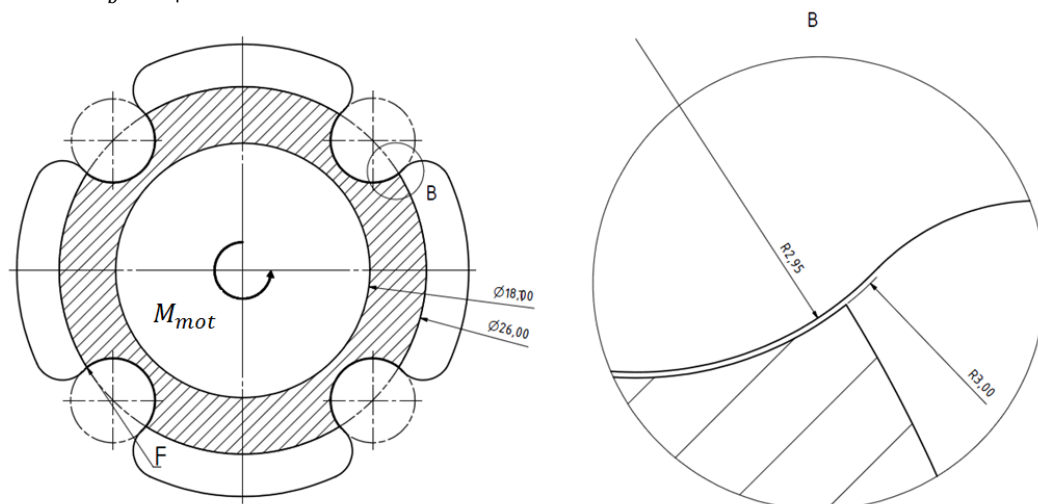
Führungsbolzen mit rinnenförmigen Nuten
